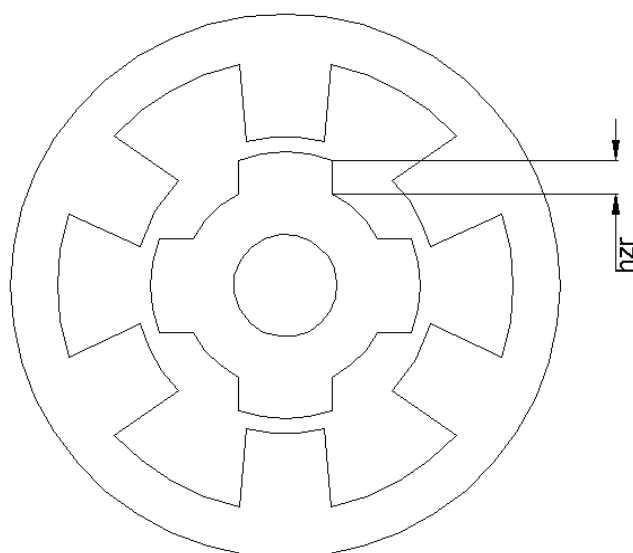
Высота полюса ротора, для трехфазного ВРД конструкции 6/4
